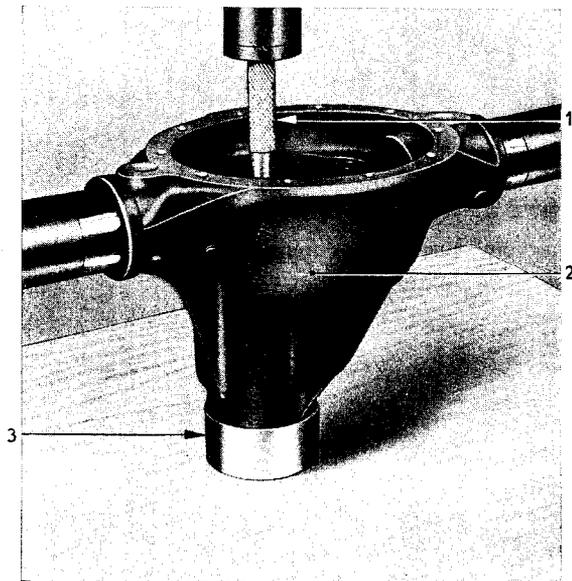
Komplettes äußeres Kegellager mit Ölblettscheibe und Dichtring unter Presse aus Hinterachsgehäuse auspressen
